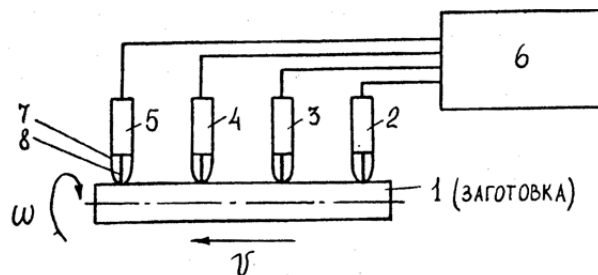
Схема способа нагрева заготовок перед штамповкой низкотемпературной плазмой (факельным разрядом)
